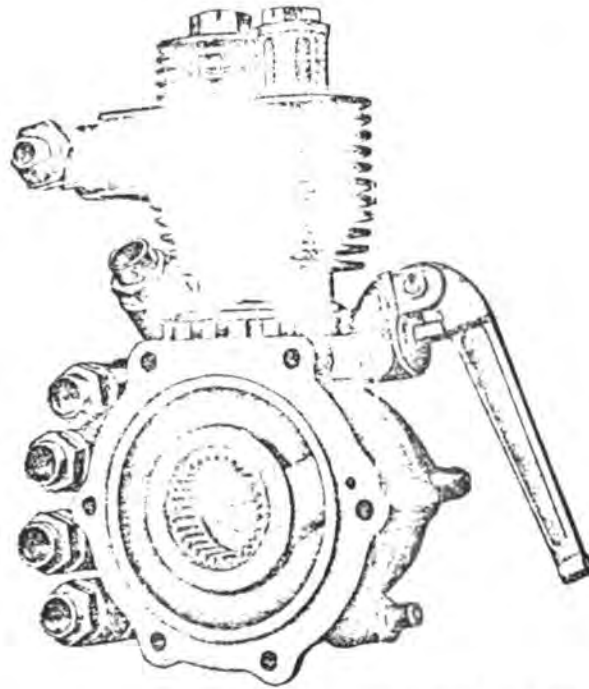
VUE ARRIÈRE DU COMPRESSEUR-DISTRIBUTEUR 'AIR-ÉQUIPEMENT'
